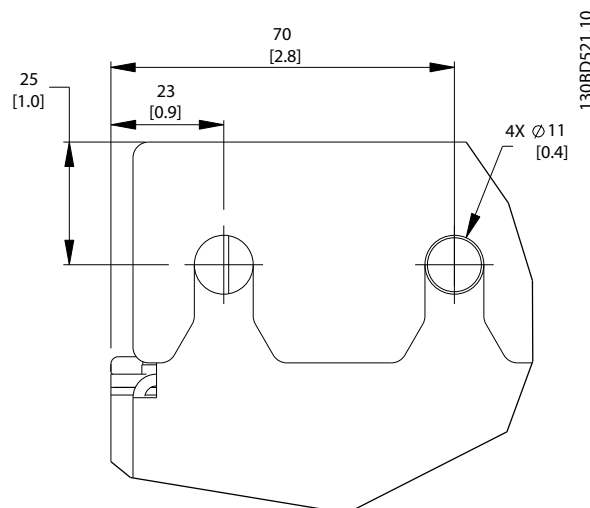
Детальный чертеж верхнего монтажного отверстия, D8h
